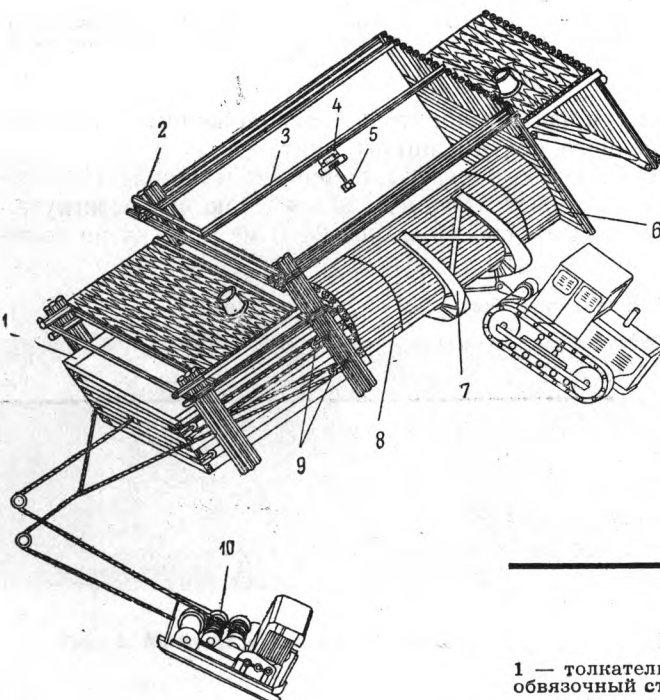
Общий вид торцовочно-обвязочного агрегата:
